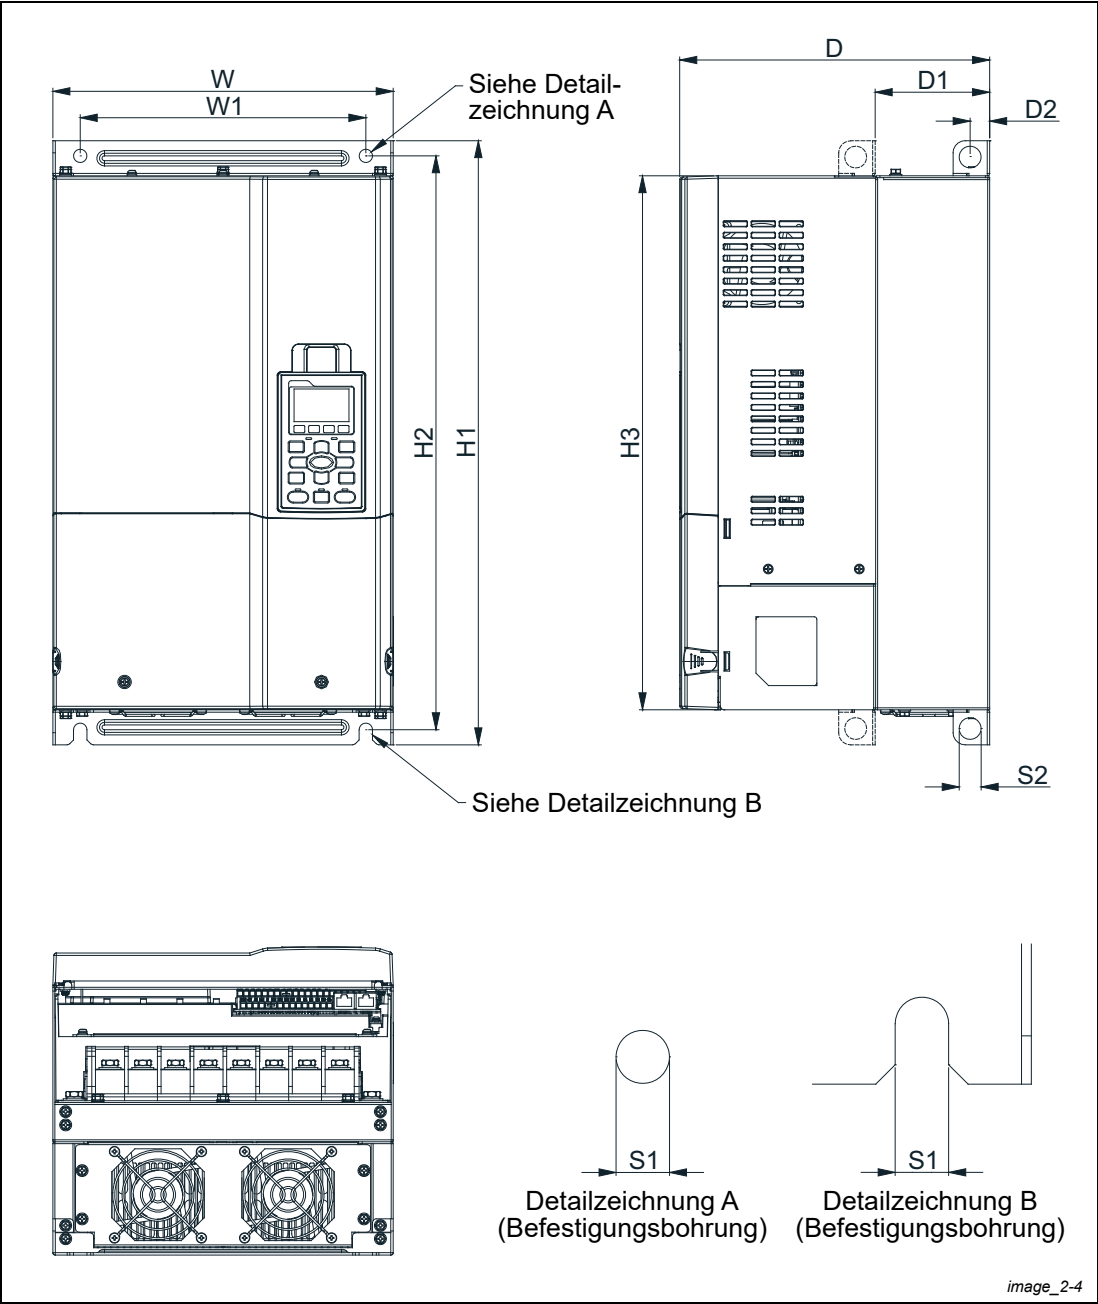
Geräteabmessungen für Baugröße D0-1
